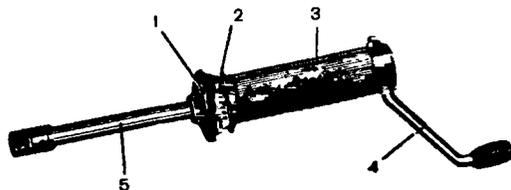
Динамометр 02.7812.9501: 1 - подвижной указатель; 2 - указатель ограничения крутящего момента; 3 - корпус; 4 - рукоятка; 5 - стержень с наконечником, вставляемым в переходную втулку гайки крепления фланца ведущей шестерни
